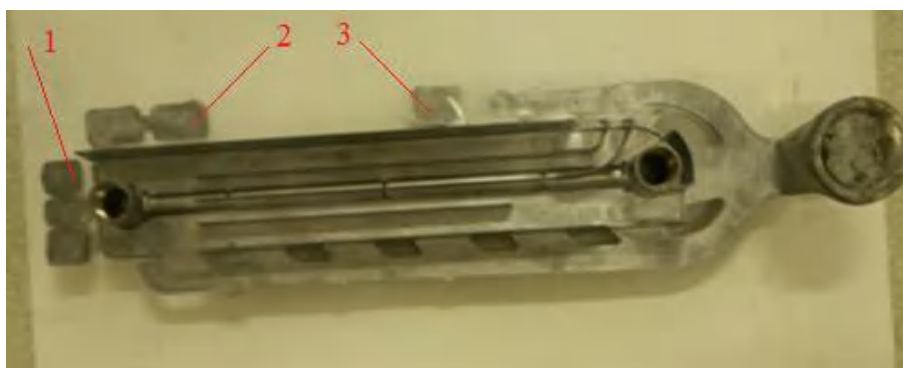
Образец № 3–2 – отливка с литниково-питающей системой:
